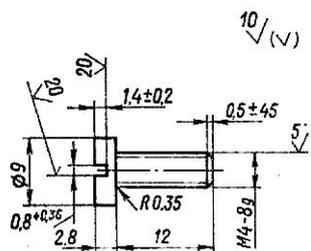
Резец для проточки внутренних стопорных канавок, короткий П83.04Л.000:
